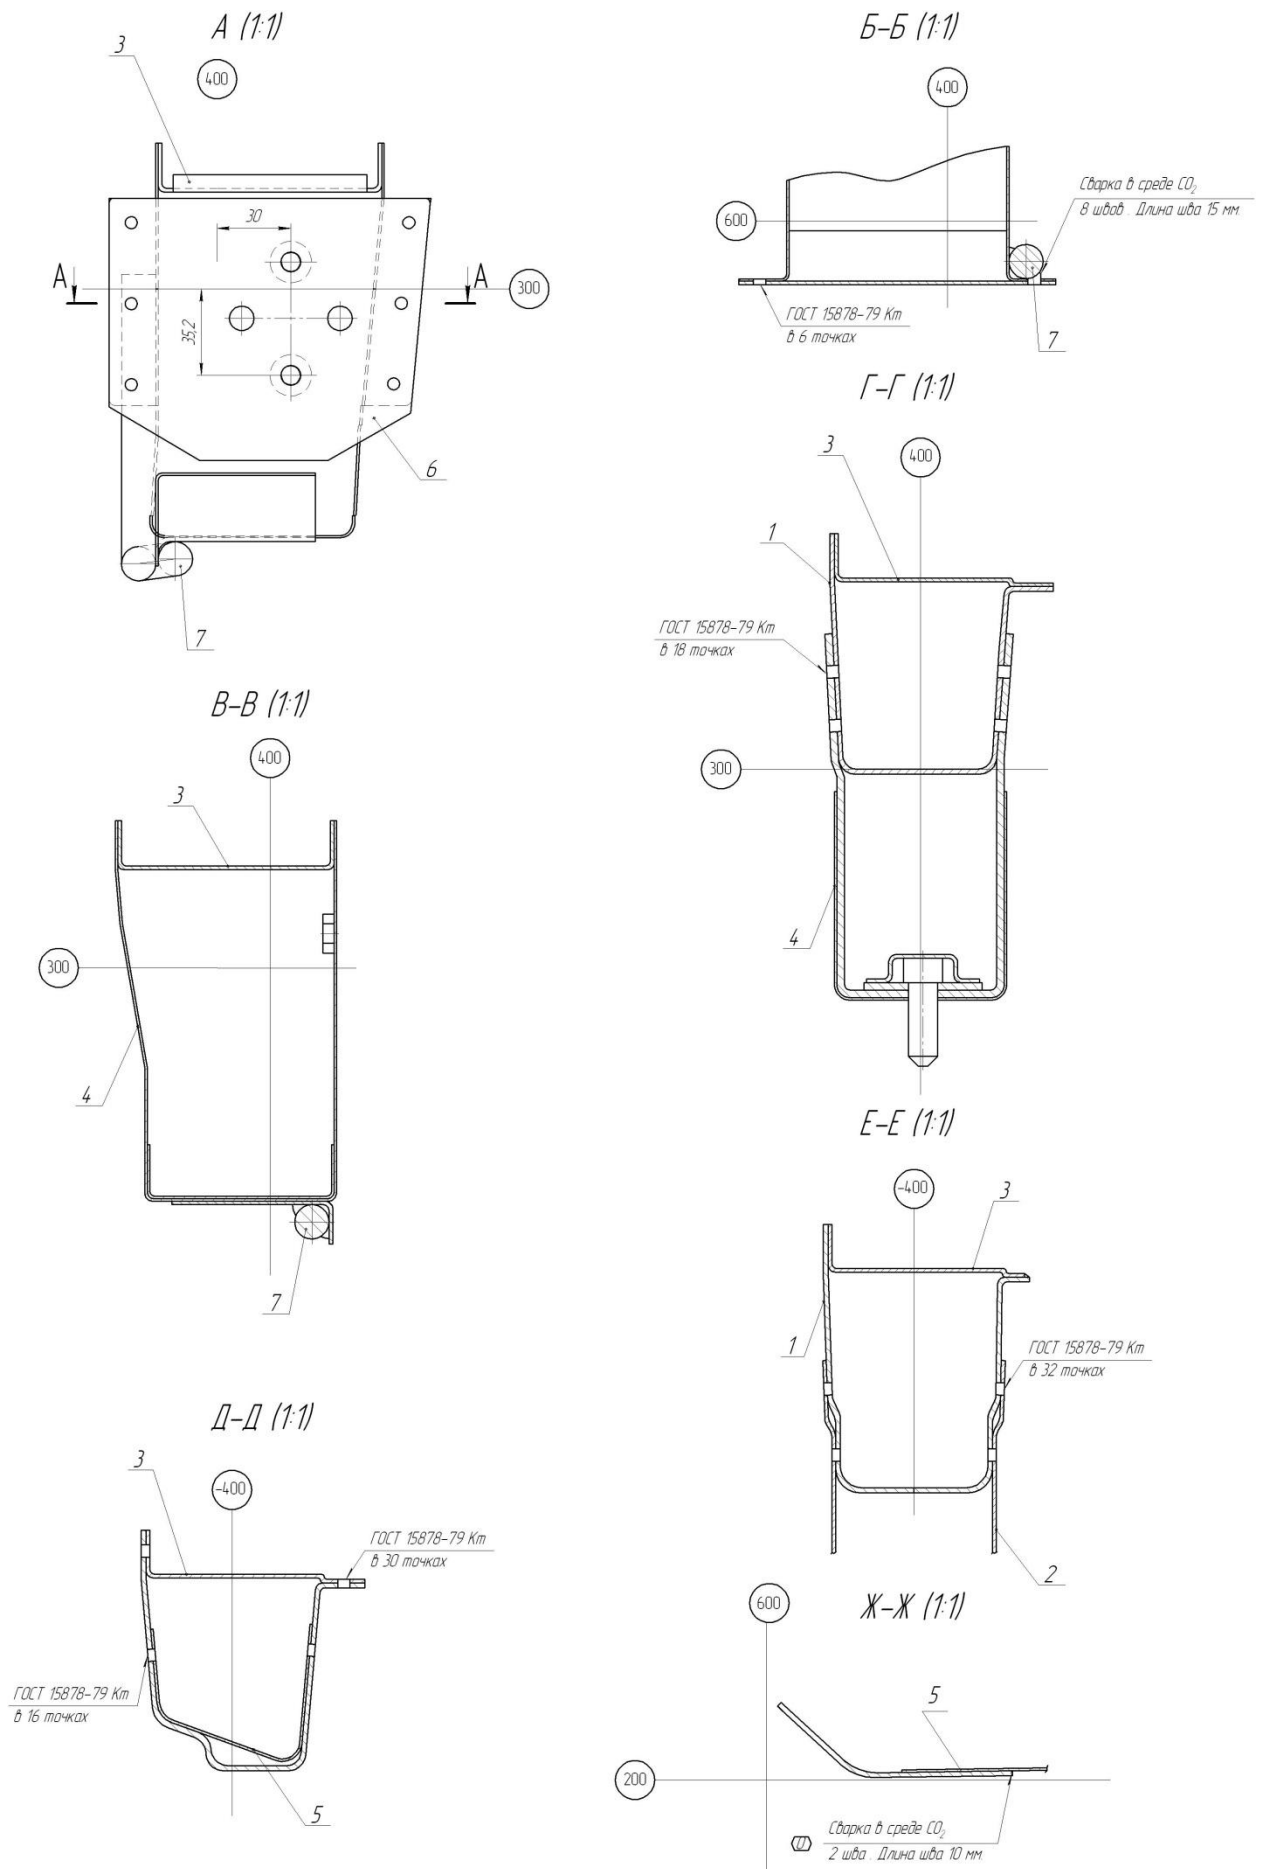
Сечения узла с указанием мест сварки
